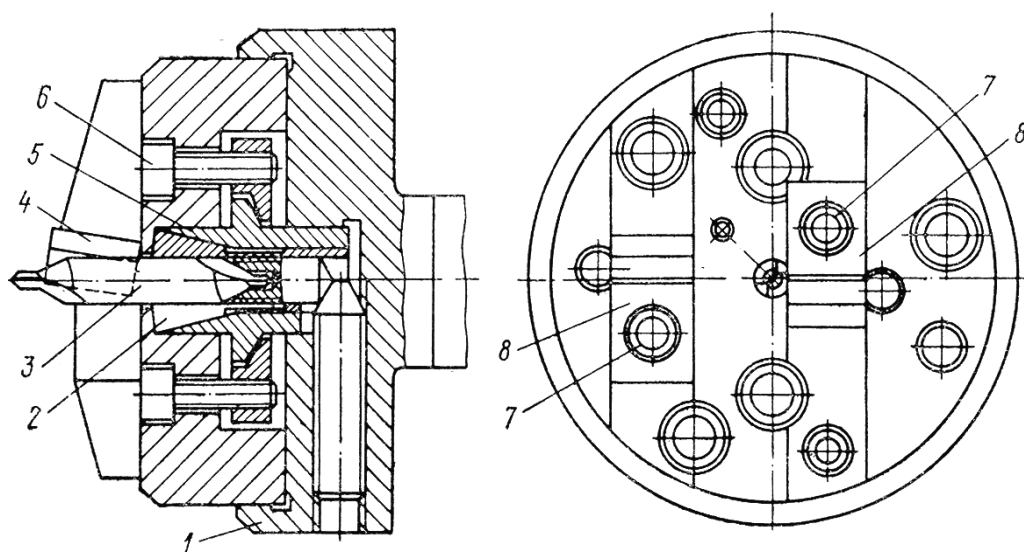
Патрон для подрезки и одновременной зацентровки торцов заготовок
